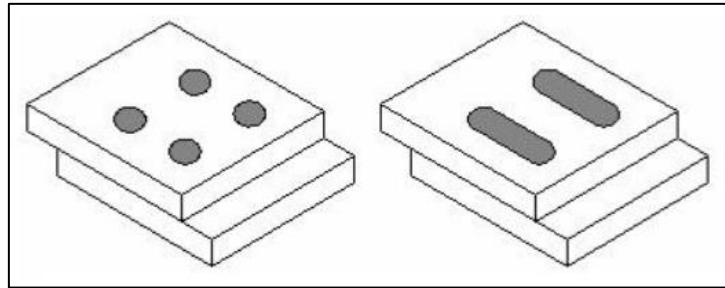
Soldaduras de tipo tapón y ranurado
